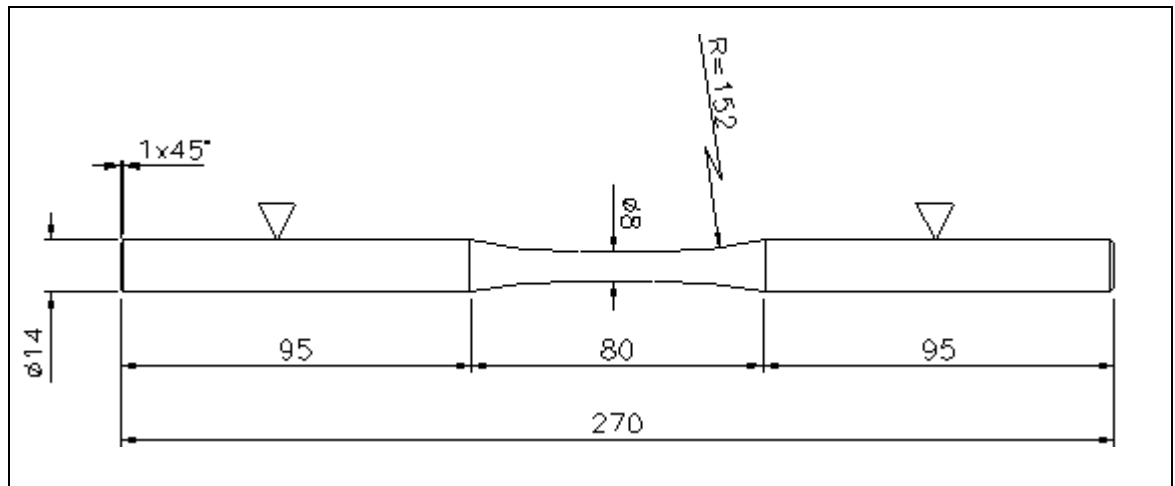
Corpo-de-prova e respectivas dimensões (em mm)
